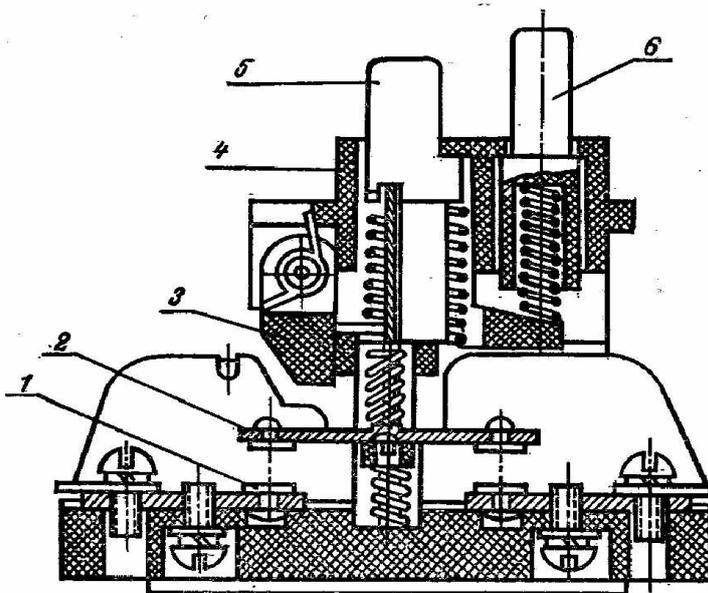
Натискний пускач серії ПНВ: 1 – нерухомі контакти; 2 – рухомі контакти місткового типу; 3 – клямка; 4 – корпус; 5 – кнопка «Пуск»; 6 – кнопка «Стоп».
